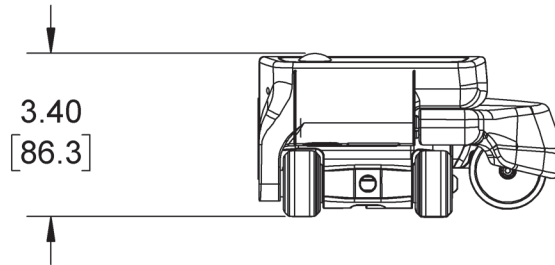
Dimensiones desde la vista frontal del HydroFORM
